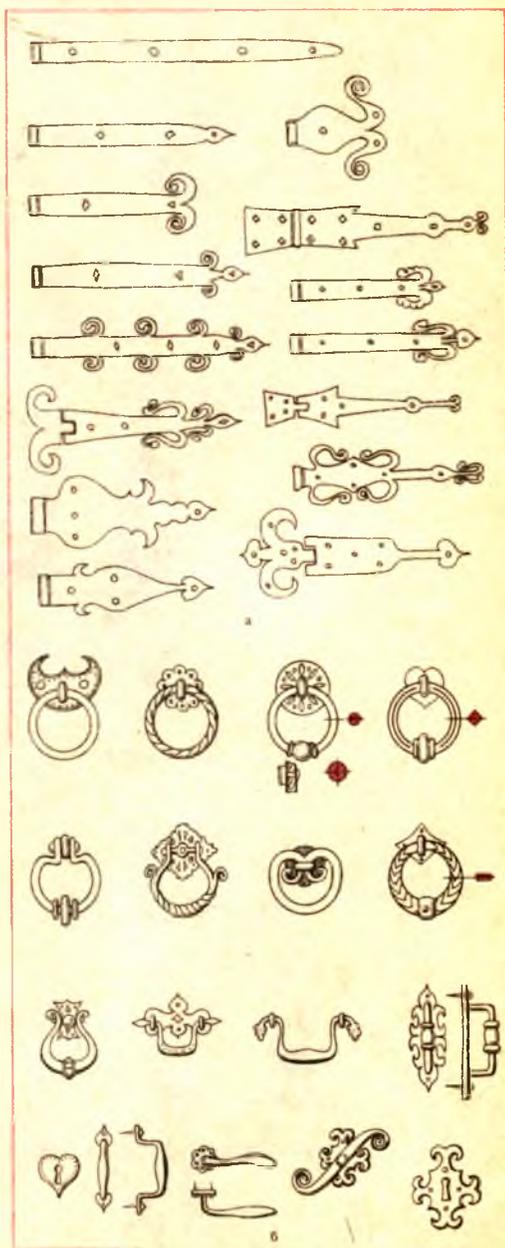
Кованые приборы дверей: а — жиковины; б — ручки, ручки-стукала, личинки
